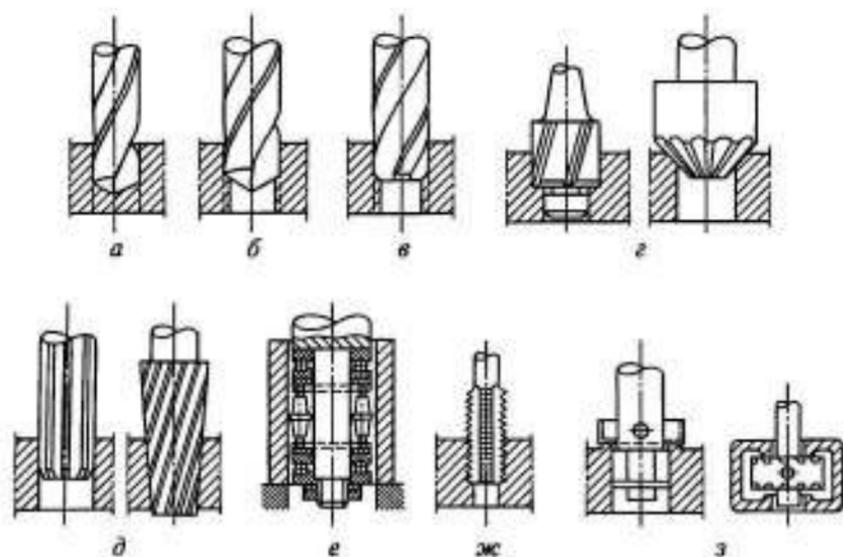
Работы, выполняемые на сверлильных станках:
